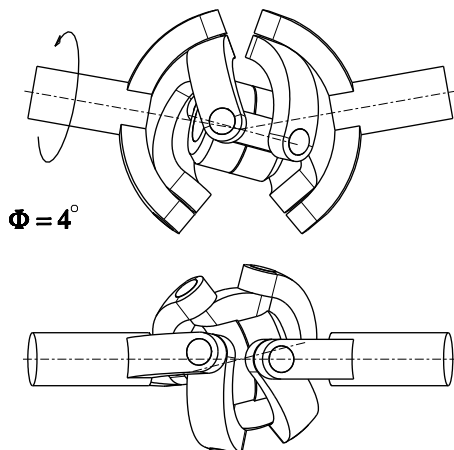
CAD model kĺbu s definovanými kinematickými väzbami (PTC CREO 2.0, modul Mechanism)
